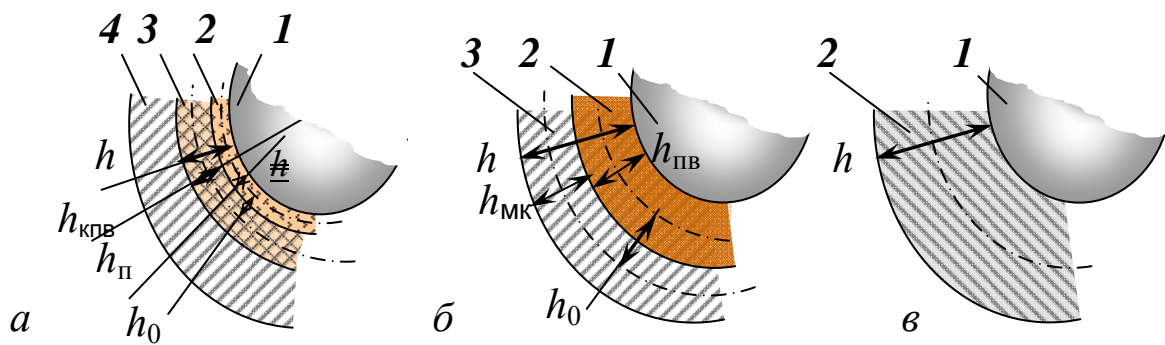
Последовательное приведение трёхслойного корпуса шарнира к эквивалентной оболочке (разрез ШО):
